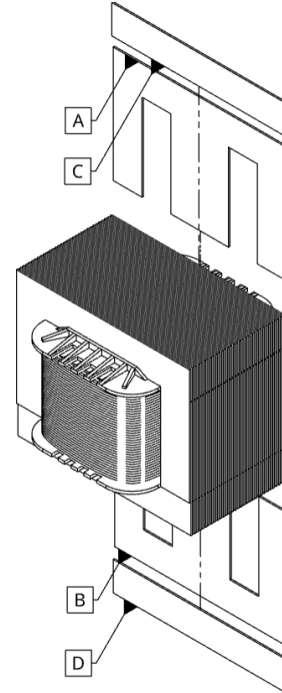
Plano de disposición de las laminas en el núcleo primero se alterna entre el paso A y B sucesivamente hasta que se tenga apretado el carrete y posterior se alterna entre el paso C y D.
